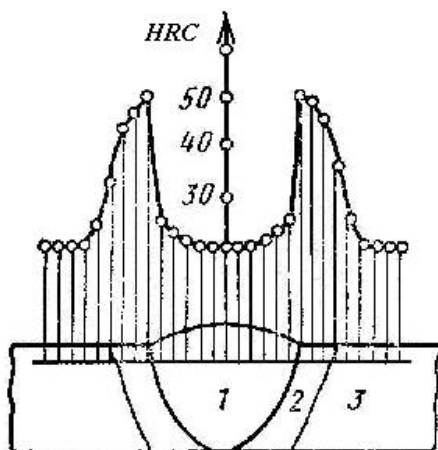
Распределение твердости после термической сварки стали 40ХФА: 1 – сварной шов, 2 – зона термического влияния, 3 – основной материал свариваемых заготовок
